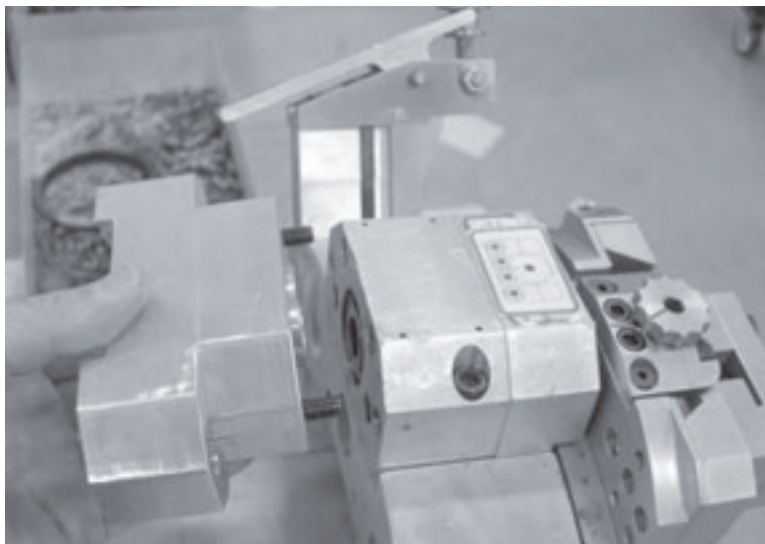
Прикрепите переходник гидравлического двигателя к корпусу ведущей шестерни.
